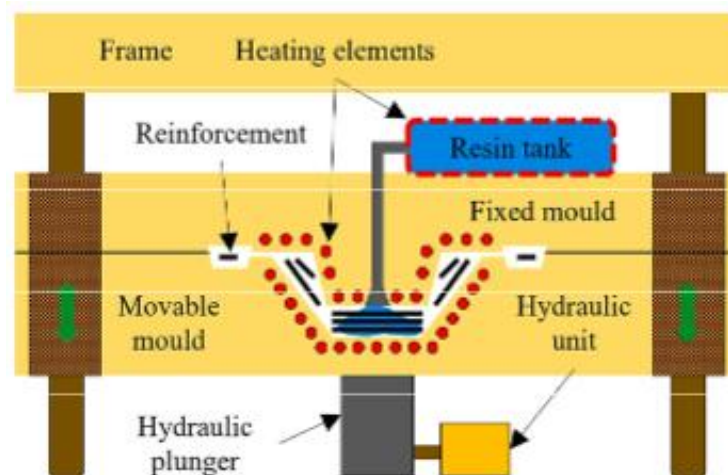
Representação esquemática da moldação por transferência de resina [36]
